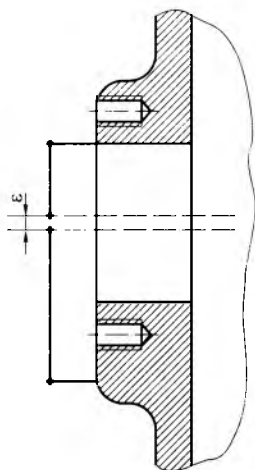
Связь отверстий под опоры валов в корпусных деталях с контурами поверхностей бобышек
